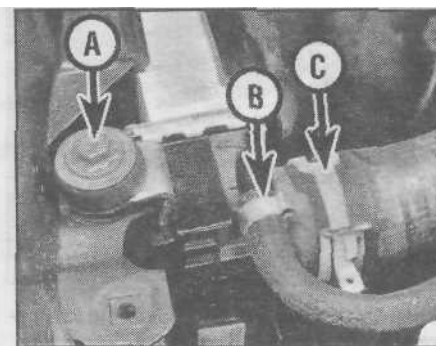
Болт крепления радиатора [A], соединение шланга расширительного бачка [B], и соединение верхнего шланга [C]
